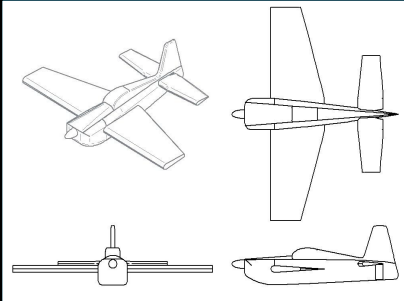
Vista de planta de la aeronave Tzauri (segunda aproximación)
